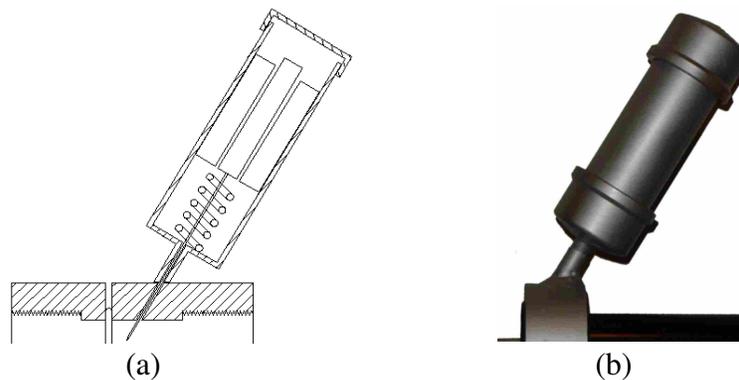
(a) Desenho esquemático do conjunto válvula solenóide; (b) Válvula solenóide.
